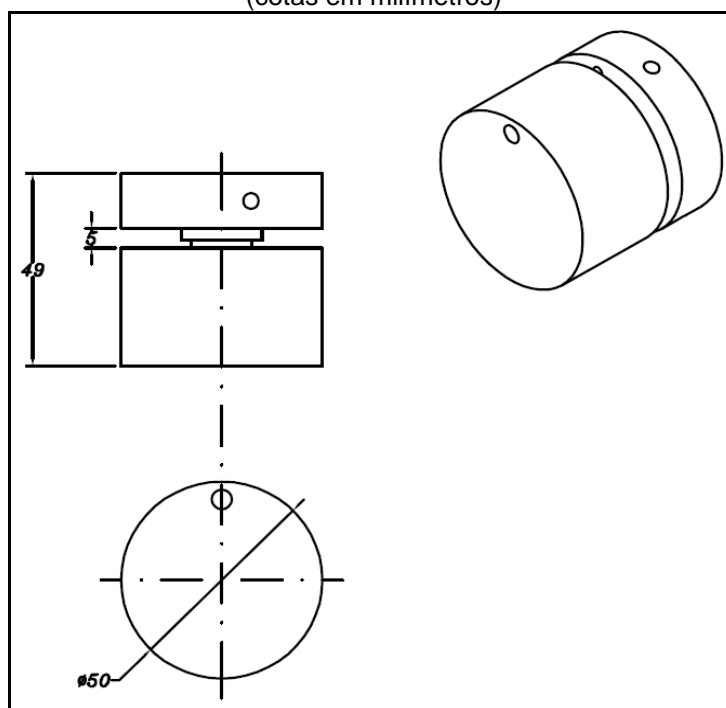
Base de fixação do rolamento e sensor (cotas em milímetros)
